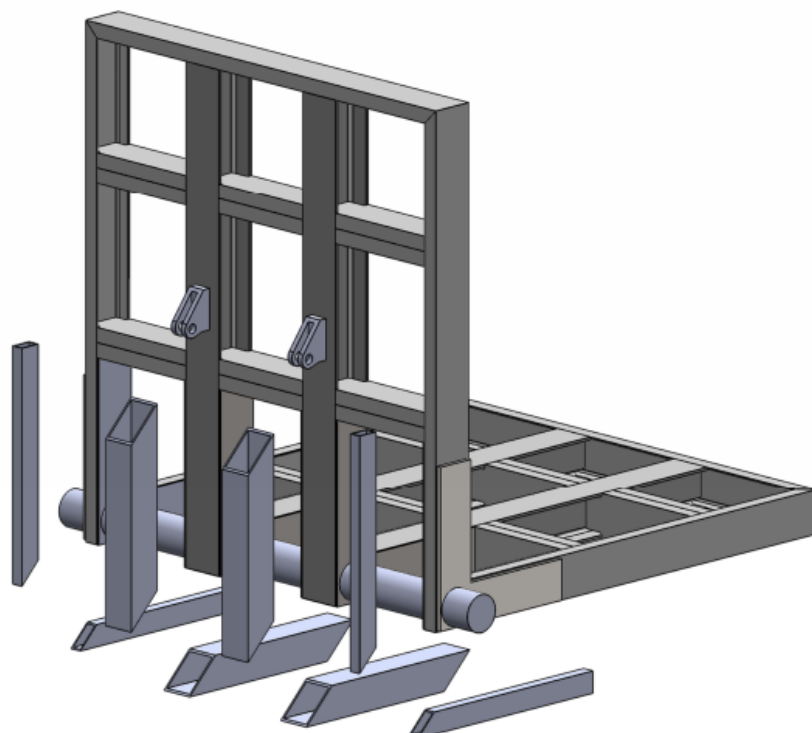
Soldadura final do subconjunto Suporte em “L”.
